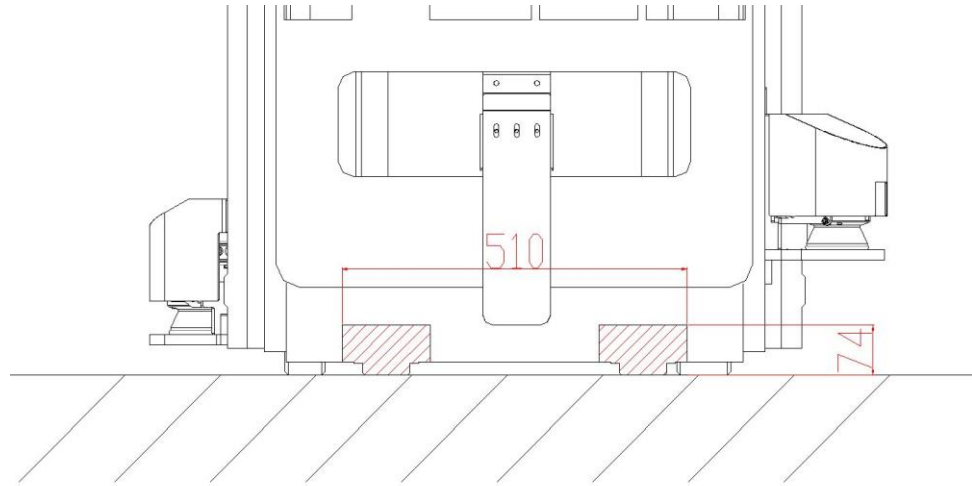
Detalle en alzado del AGV EGV-S20
